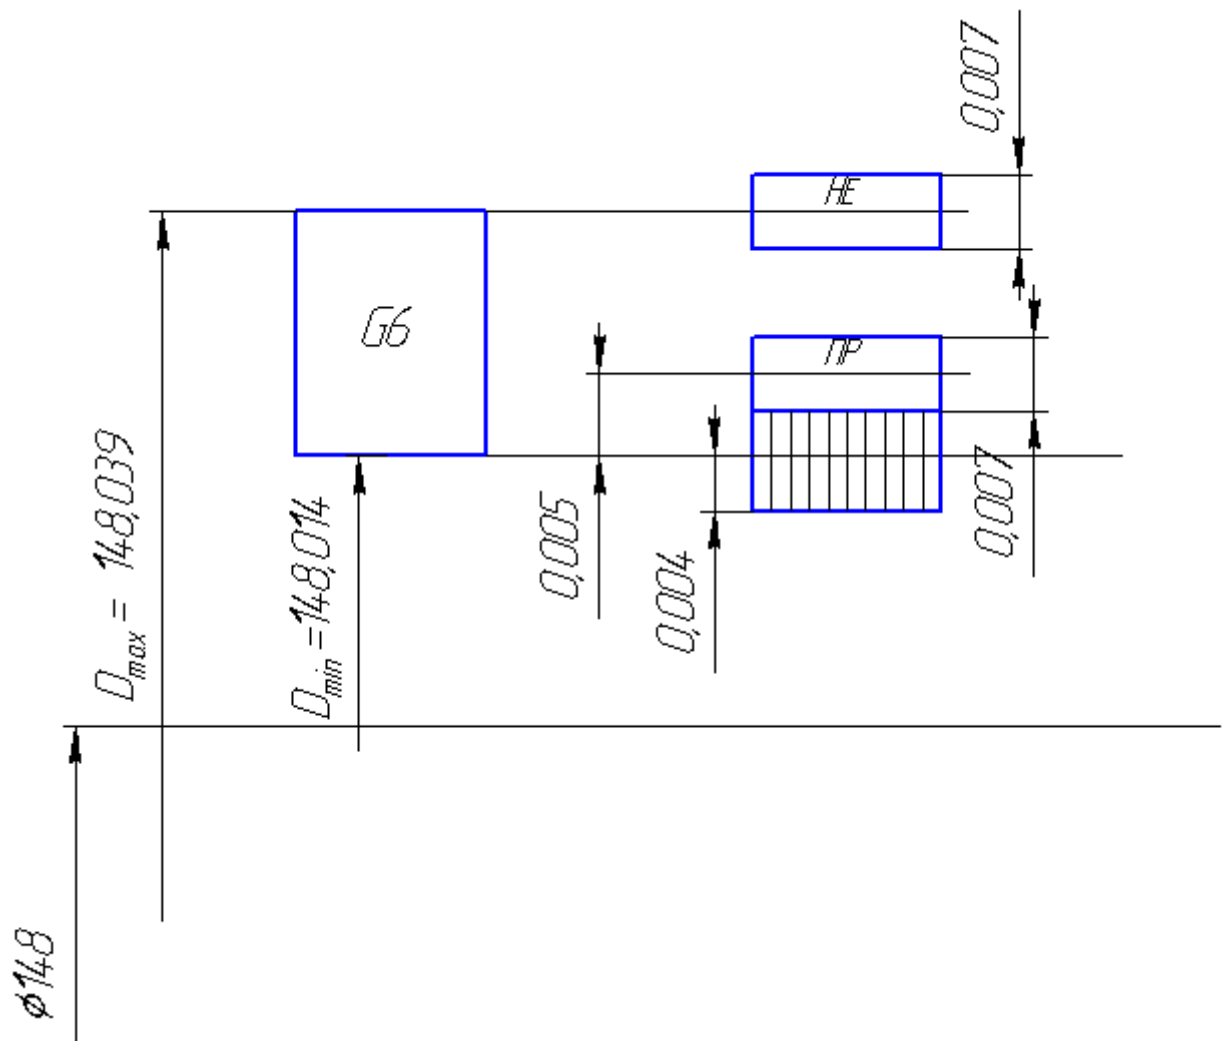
Схема расположения полей допусков калибра – пробки
